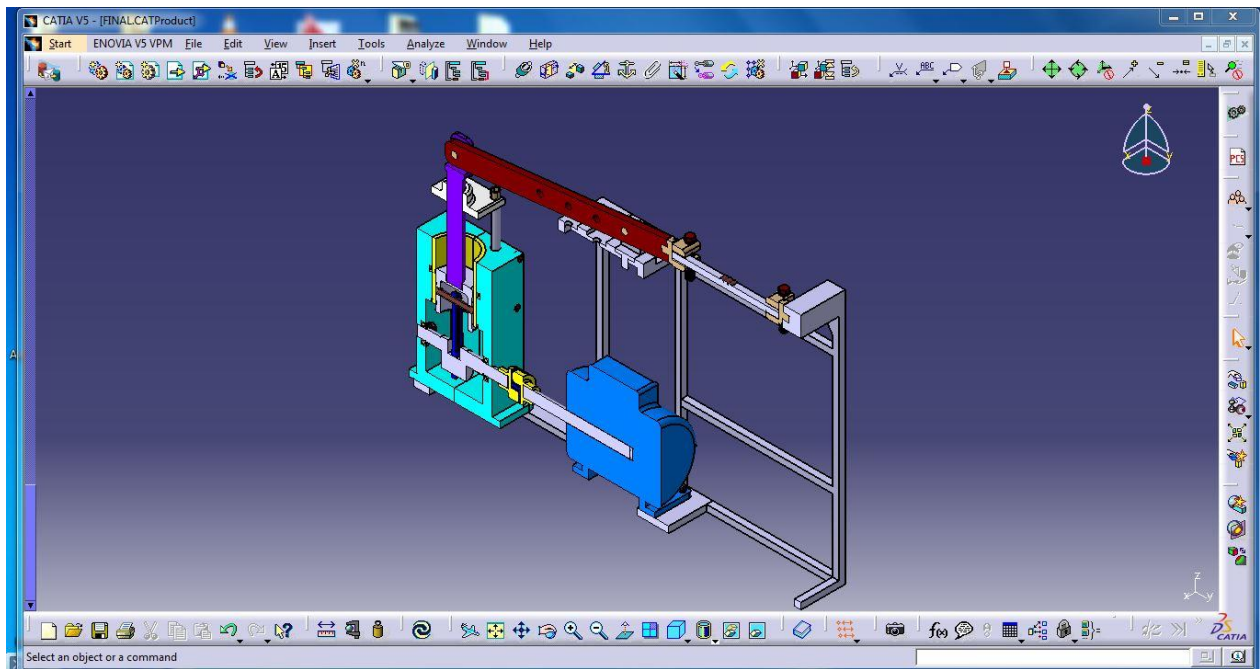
vue en coupe de la machine réalisée sur CATIA
